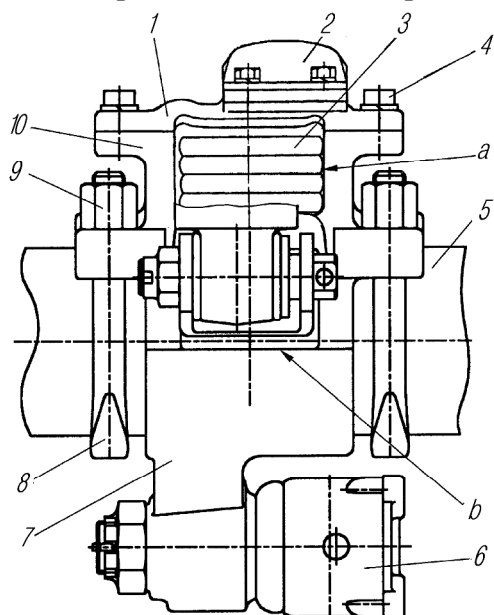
Установка опорного кронштейна передней правой рессоры (вид спереди):
